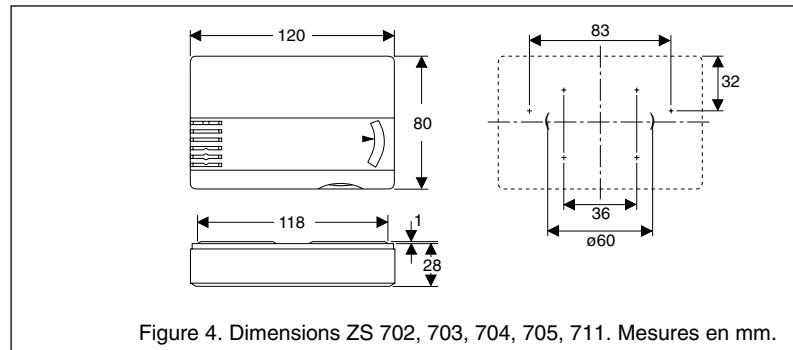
Dimensions ZS 702, 703, 704, 705, 711. Mesures en mm.
